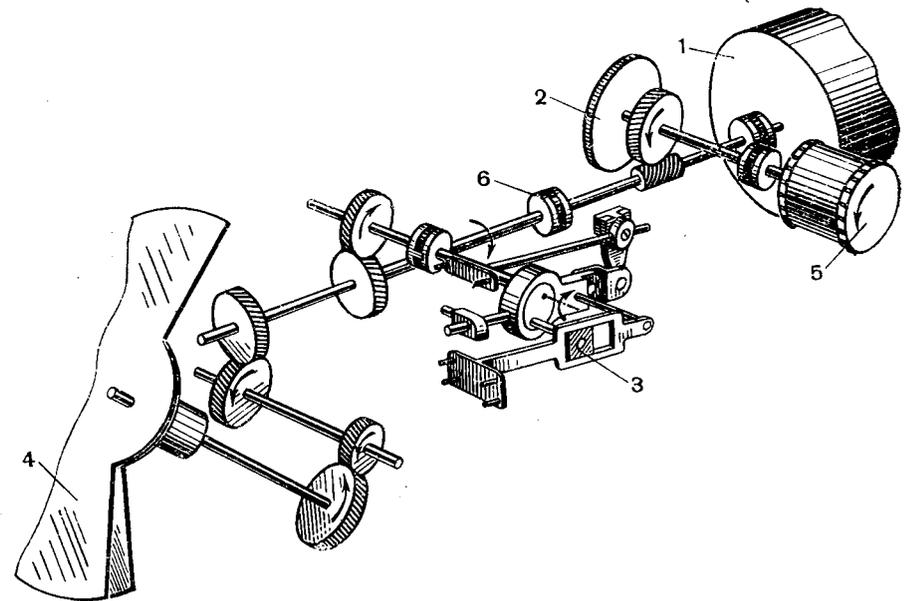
Кинематическая схема аппарата «Мир»: 1 — электродвигатель, 2 — передача на ось зубчатого барабана, 3 — грейферный механизм, 4 — обтюратор, 5 — зубчатый барабан, 6 — муфта, соединяющая две части главного вала
